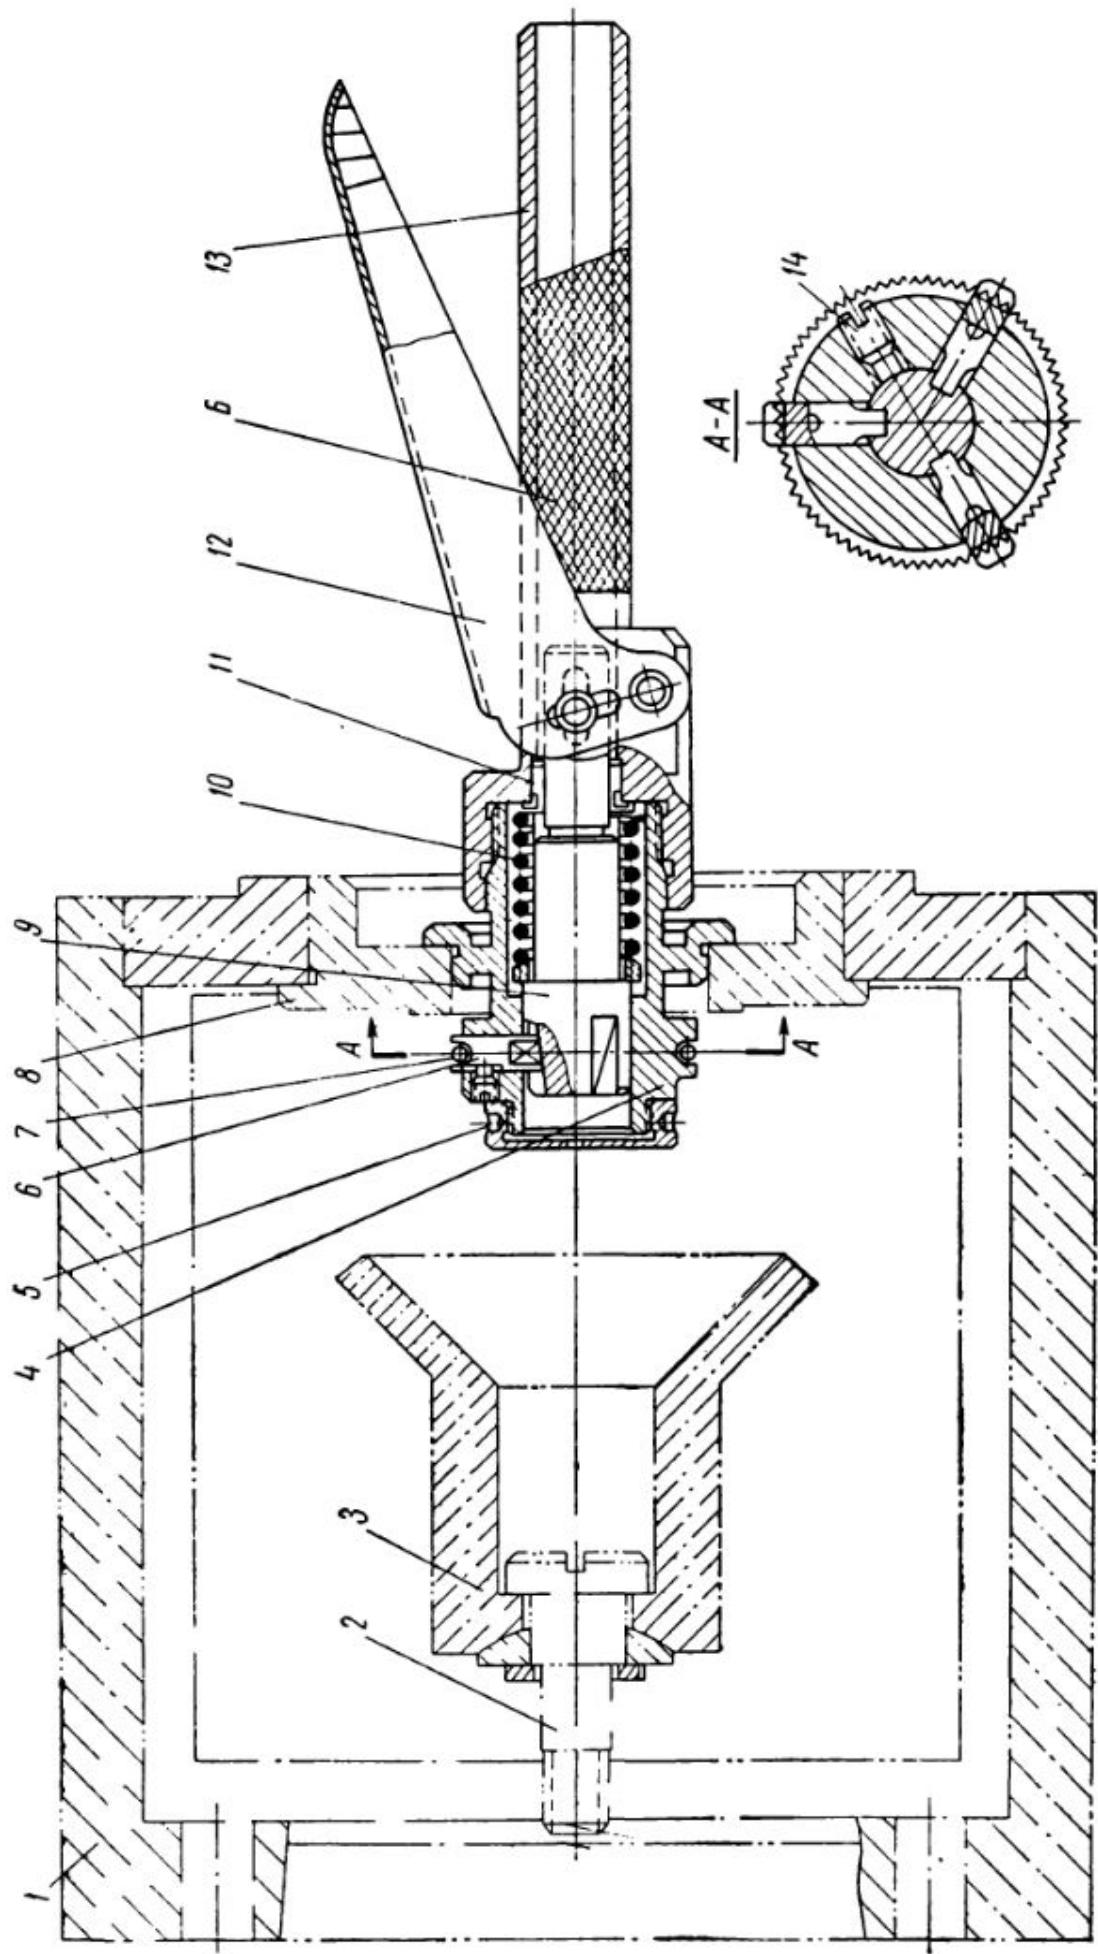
Приспособление для центрирования и закрепления шарошки, показанной на рис. 25
